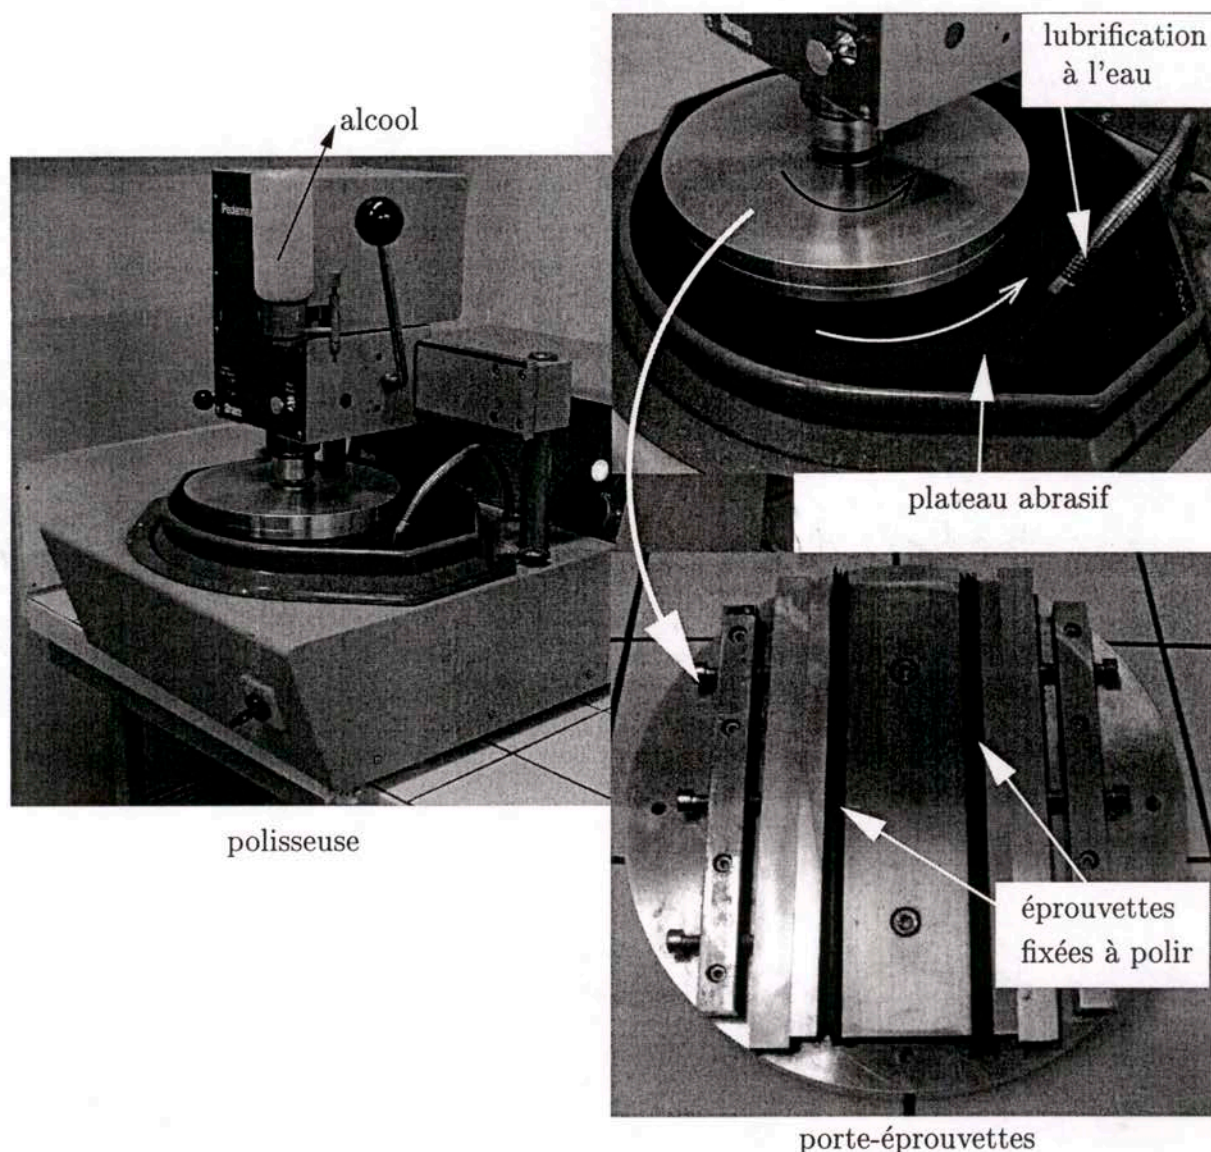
Dispositif de polissage du bord des éprouvettes.
